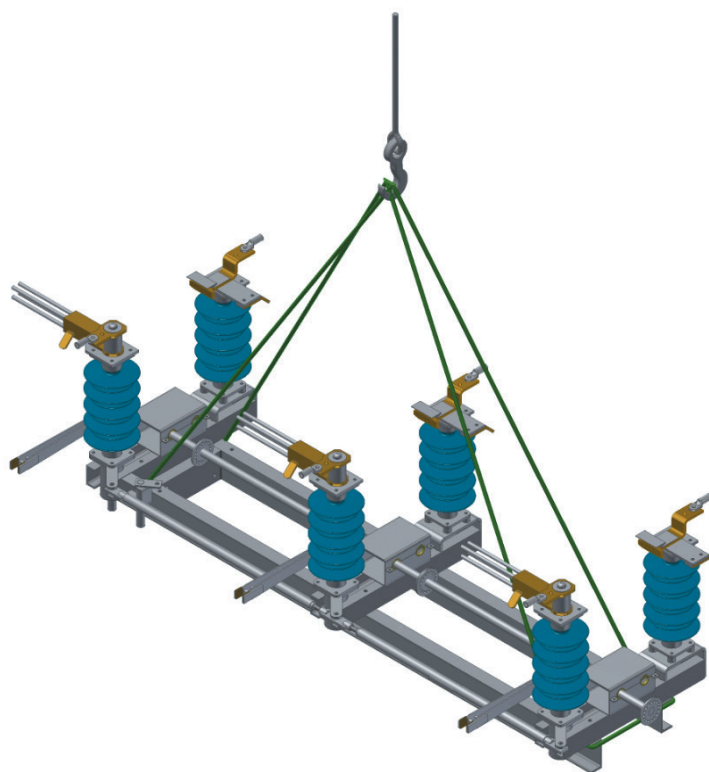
Схема строповки разъединителя типа РГПЗ-СЭЩ-35 для монтажа на стойку монтажную
